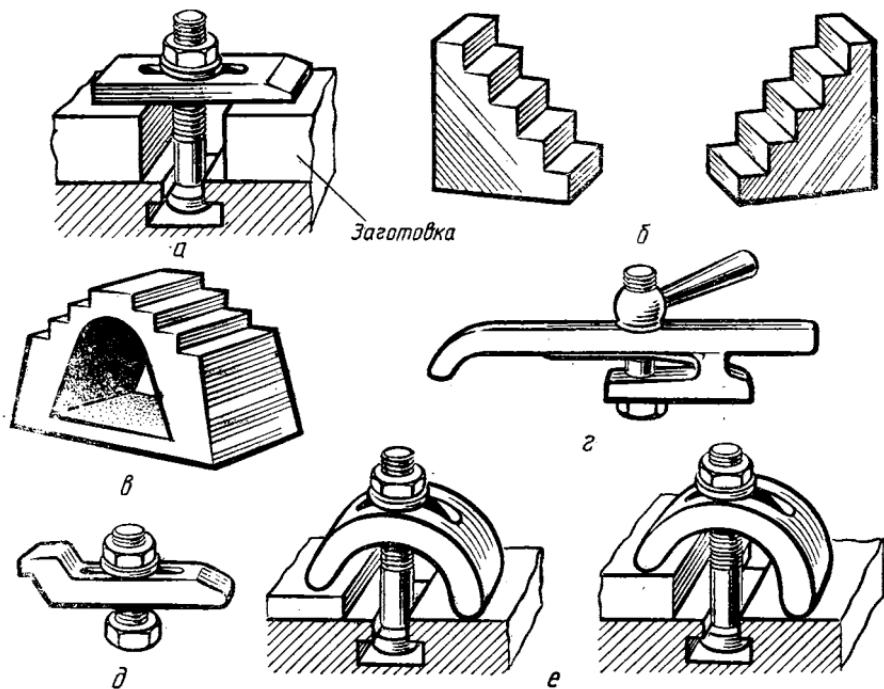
Приспособления для закрепления заготовок на столе фрезерного станка:
